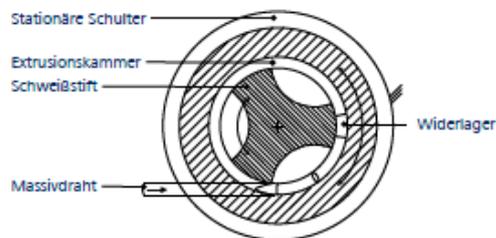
Funktionsprinzip des bewegungsentkoppelten Werkzeuges in der Schnittansicht.
